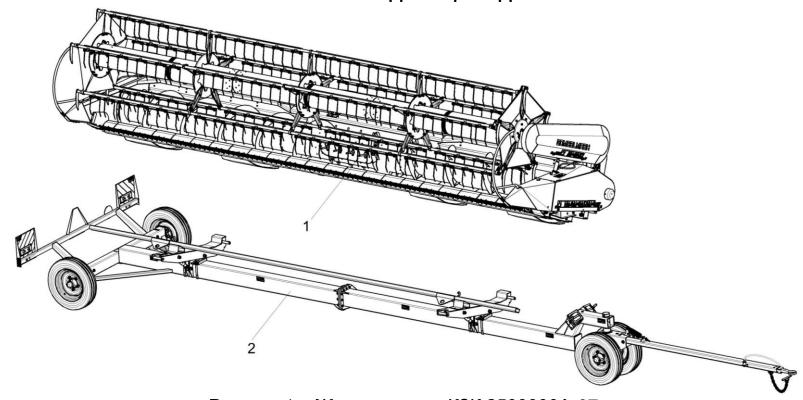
Жатка для сои КЗК 2500000А-07
